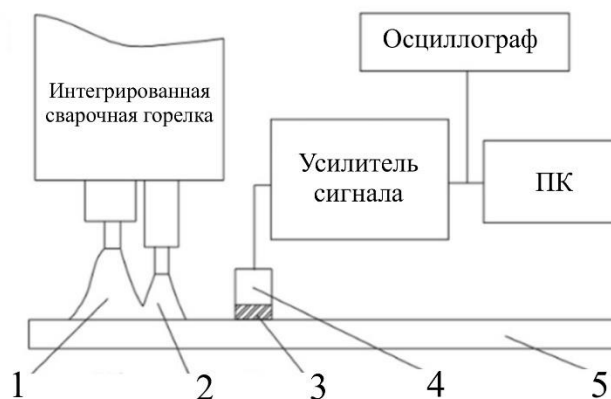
Схема двухдугового метода сварки неплавящимся электродом [48]:
